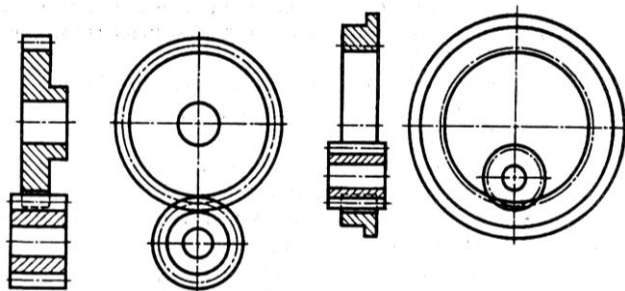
Условное изображение зубчатых передач с цилиндрическими колесами
